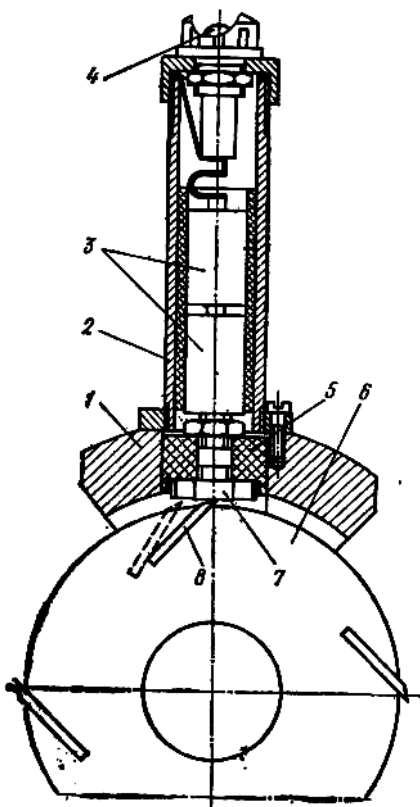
Контрольно-установочное приспособление с базированием на наружной поверхности корпуса ножевого вала:
